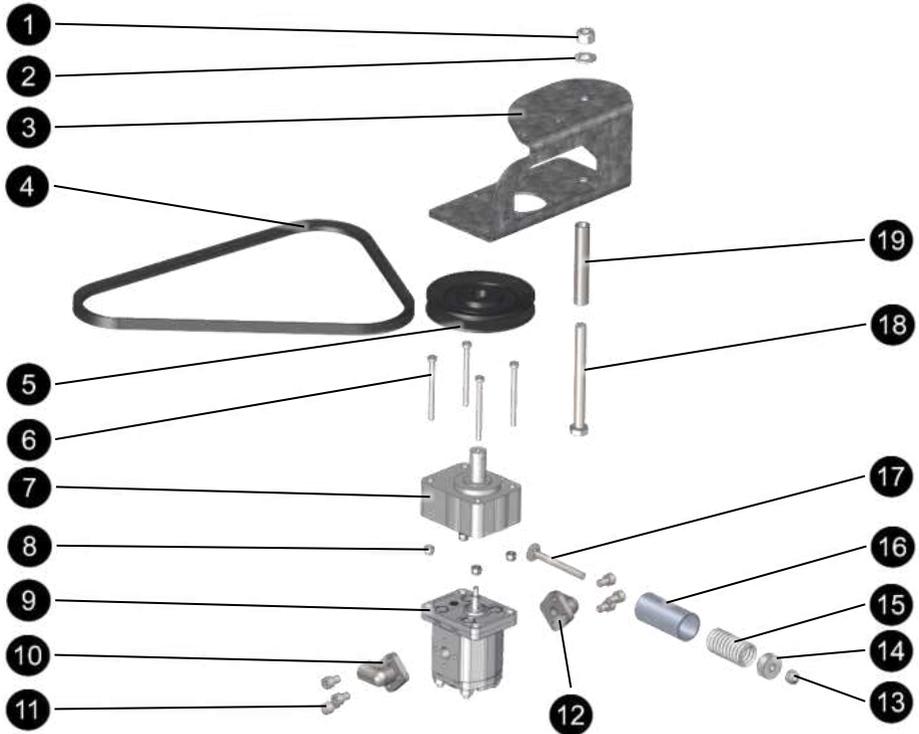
Ersatzteile Halter Hydraulikpumpe
